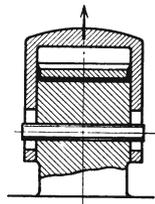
Preßluftkolben durch Eigengewicht entspannend.
